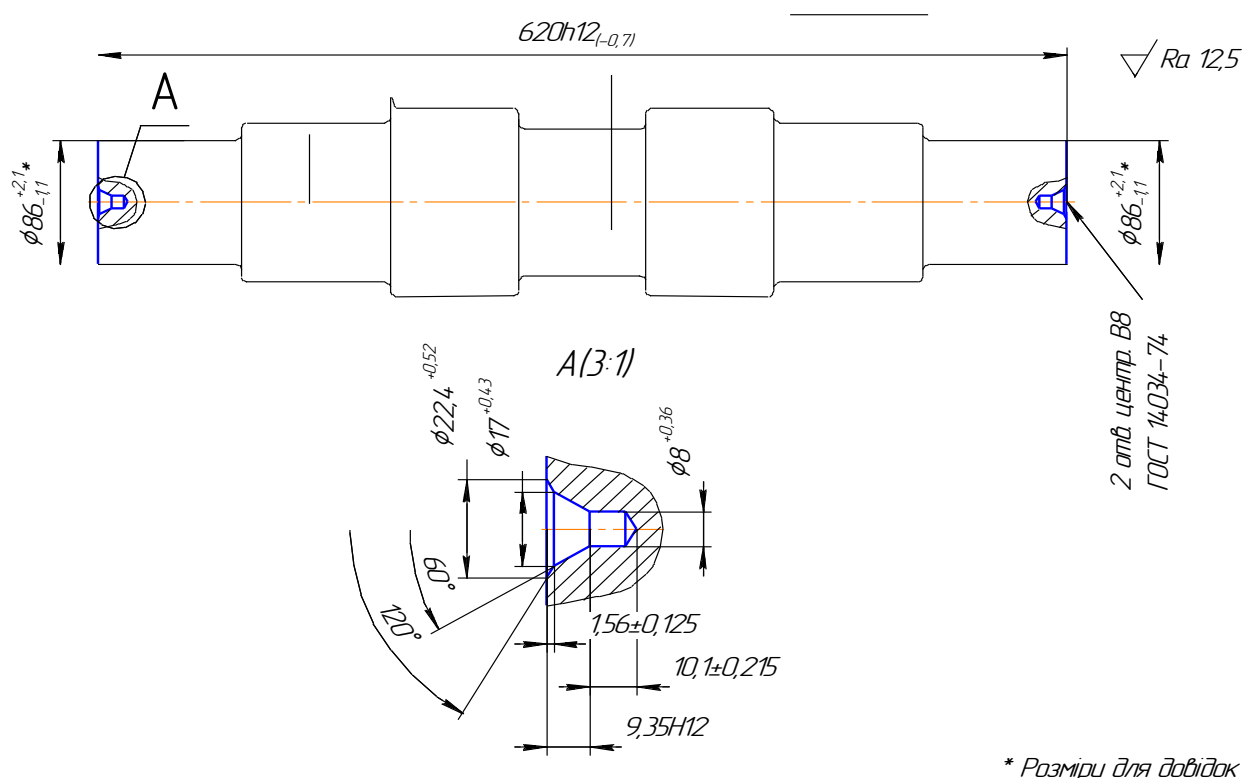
Ескіз фрезерно-центровальної операції 030
